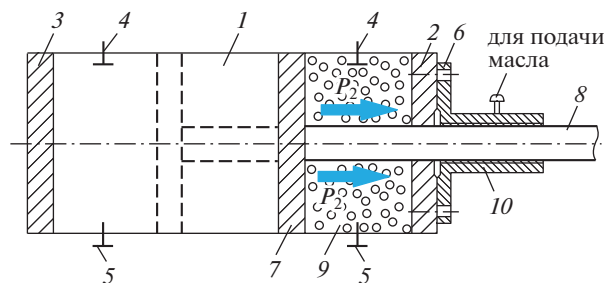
Схема воздействия давления дожимающего газа в первой ступени компрессорного цилиндра на сальниковый уплотнитель: 1 – компрессорный цилиндр; 2 – передняя крышка цилиндра; 3 – задняя крышка цилиндра; 4 – всасывающие клапаны; 5 – нагнетательные клапаны; 6 – грандбукса; 7 – поршень первой ступеньки; 8 – шток поршня; 9 – дожимающий газ, постоянно находящейся в вихревом турбулентном движении; 10 – уплотнитель.
